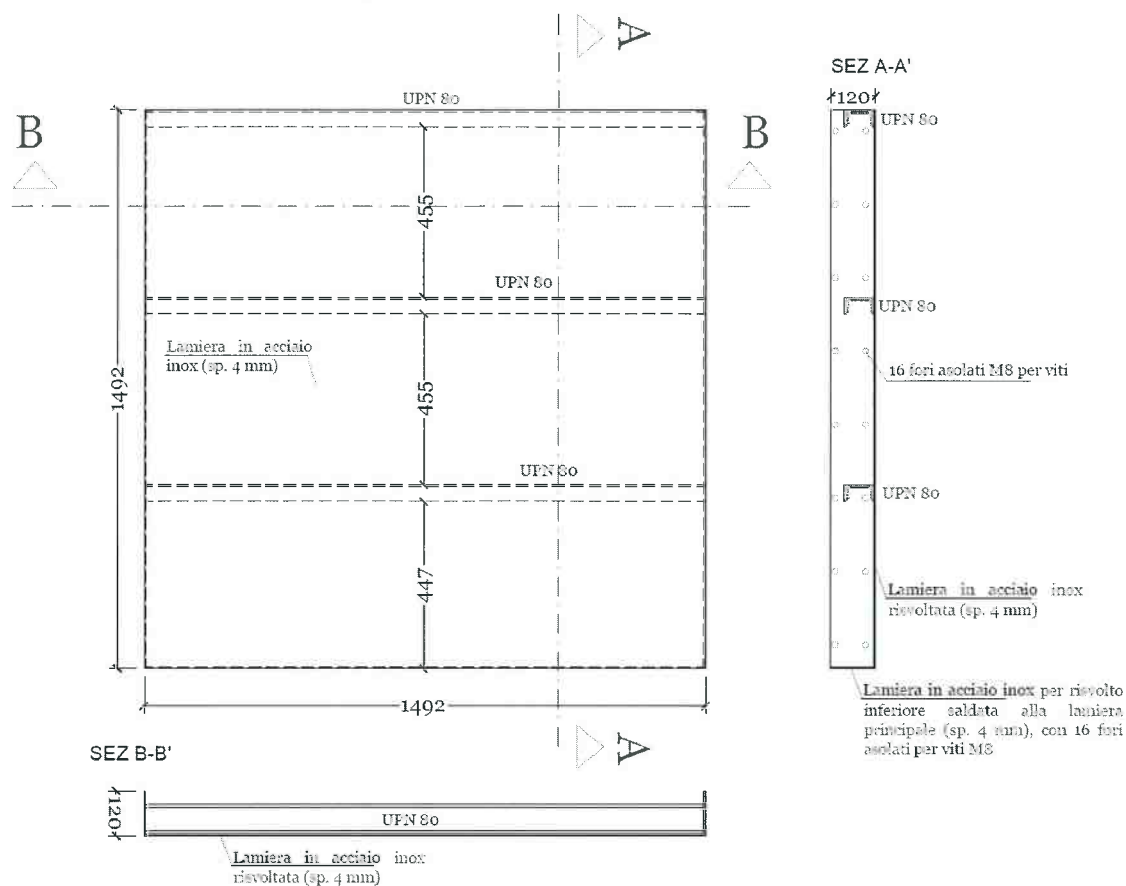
Vista in prospettiva e sezioni dell'elemento costruttivo: parete laterale tipo 2
